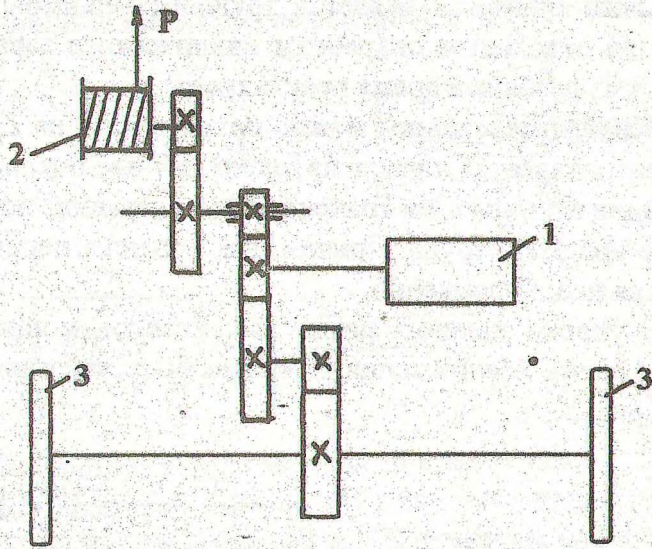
Кинематическая схема привода машины с механической лебедкой: 1 - двигатель; 2 - барабан лебедки; 3 - колеса
